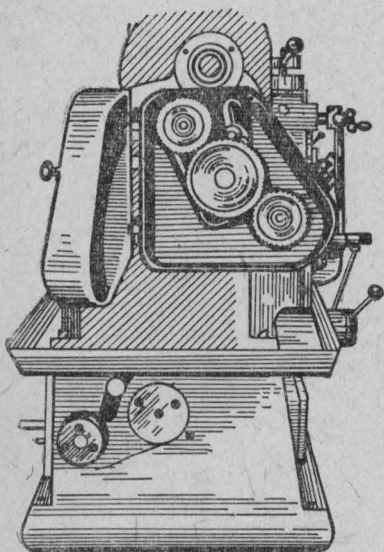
Открывающееся ограждение сменных шестерён токарного станка
